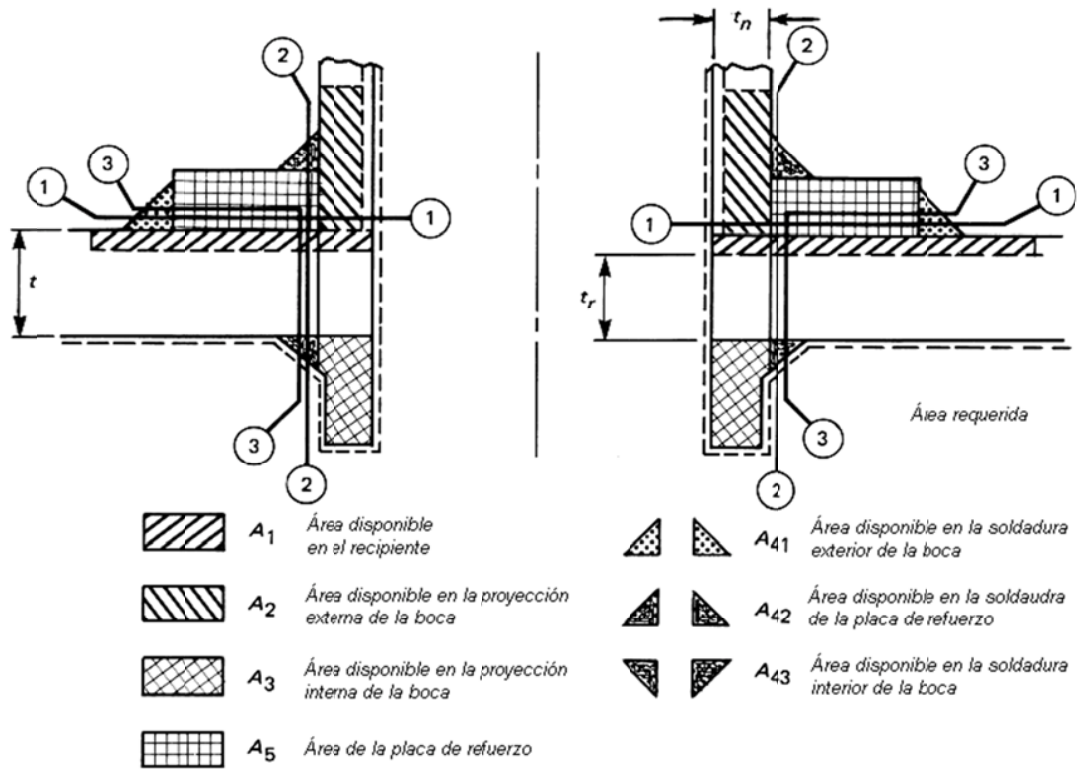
Cargas en las juntas de soldadura (bocas insertadas)⁴⁷
